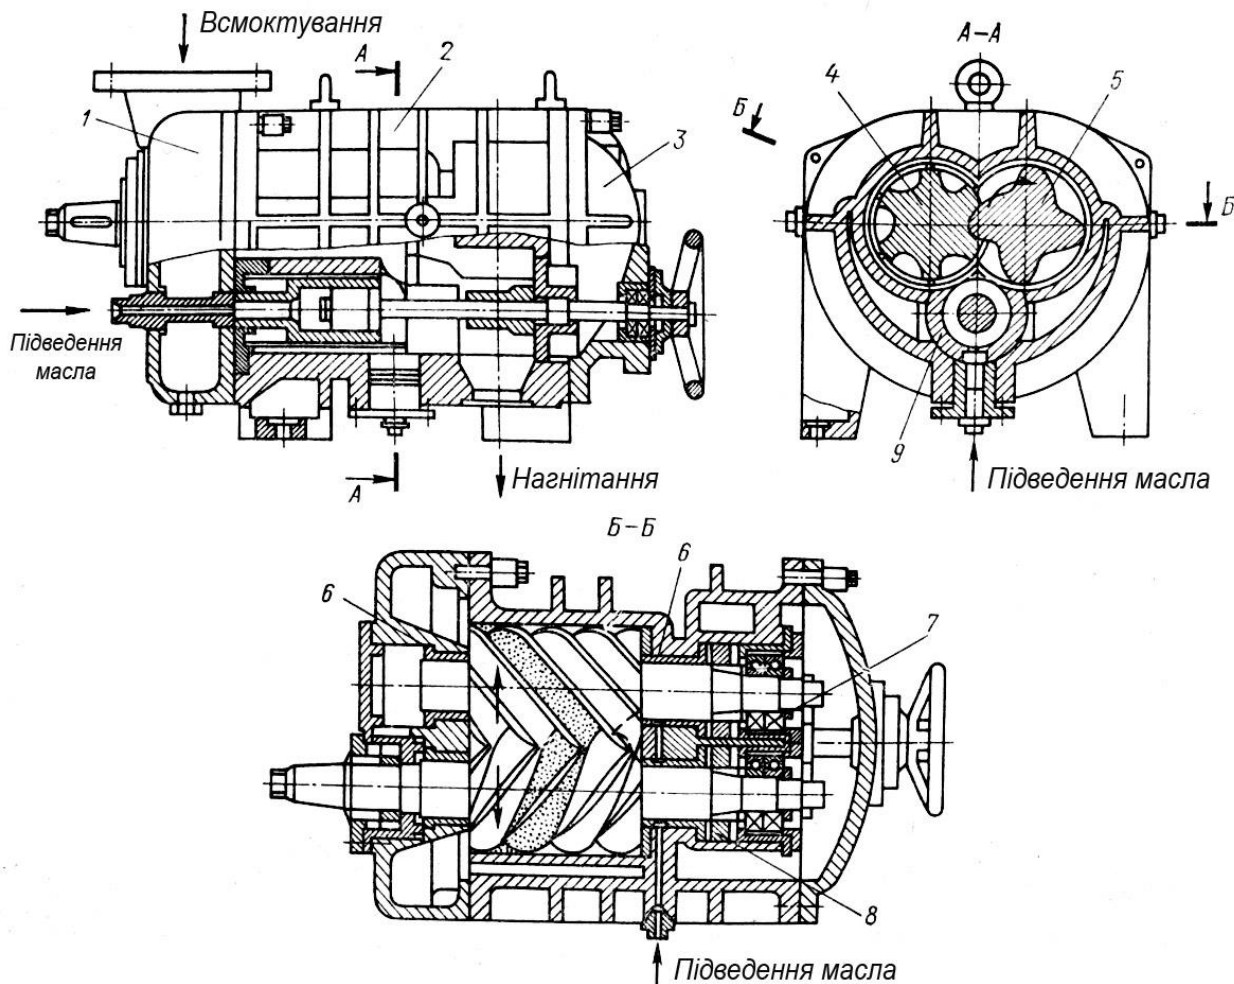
Двороторний гвинтовий маслозаповнений компресор
